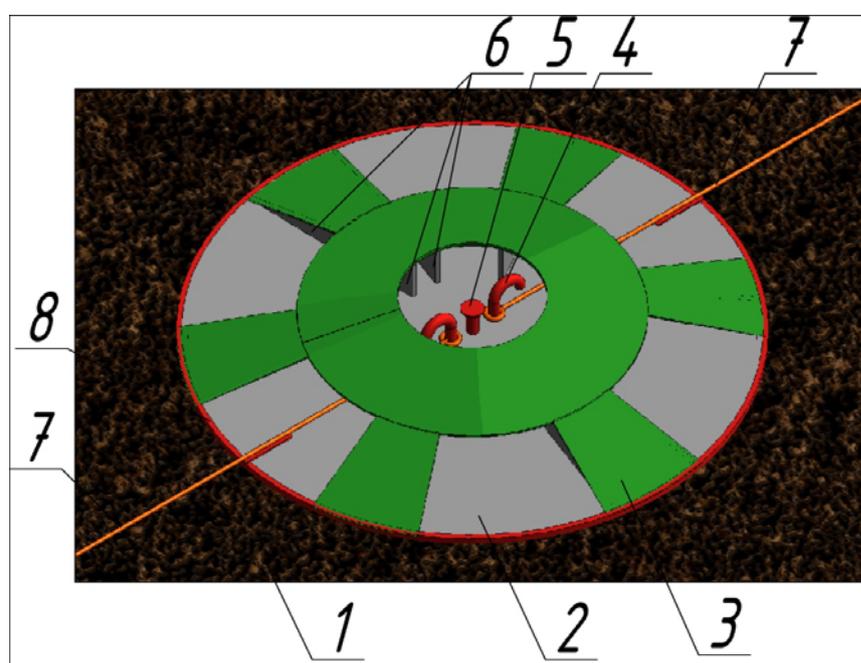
Устройство в рабочем положении: 1 – поверхность земли, 2 - металлический диск, 3 – защитный кожух, 4 – крюки, 5 – штырь, 6 – ребра жесткости, 7 – нить
